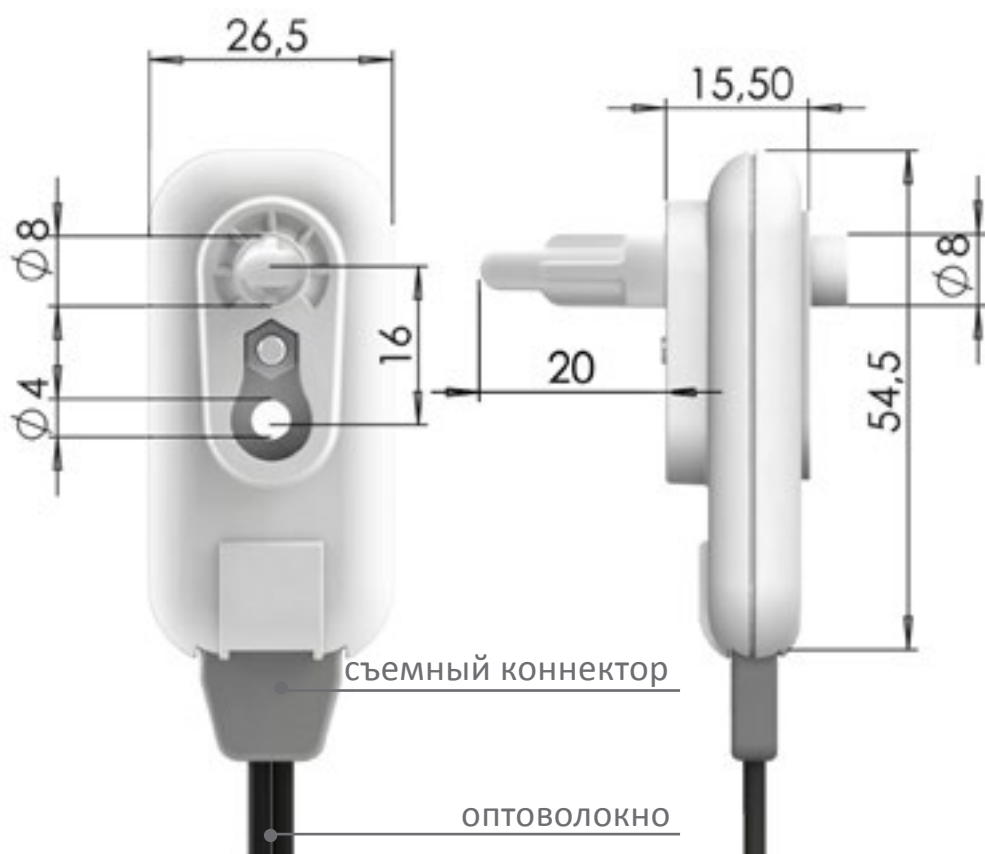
Внешний вид и габаритные размеры объектива ВОД
